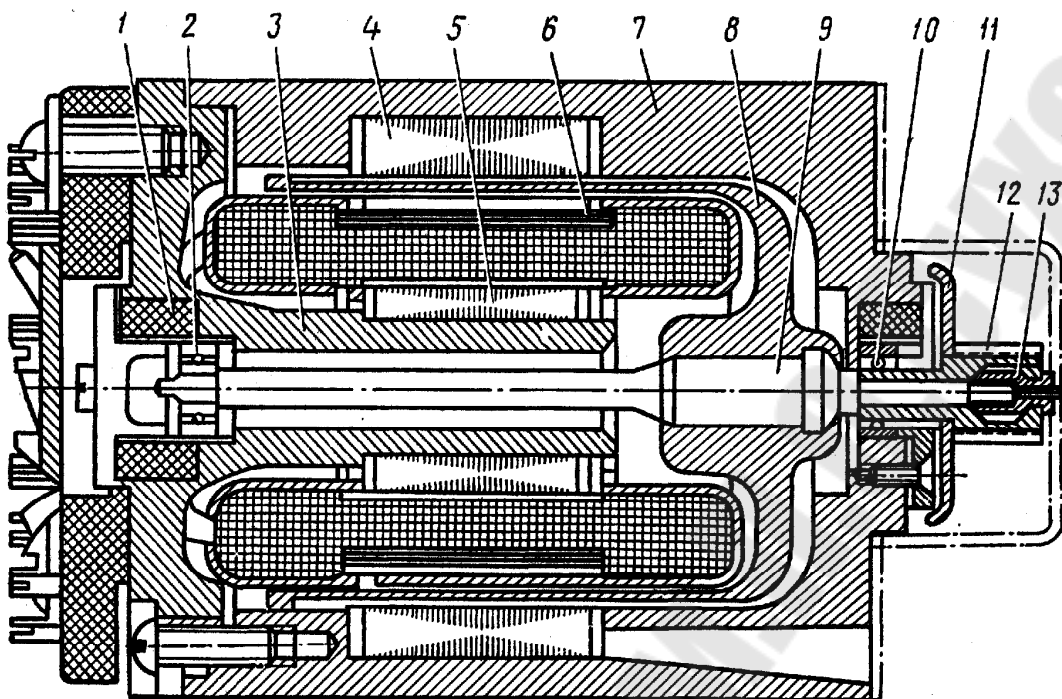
Двигатель с полым немагнитным ротором ДИД-0,6-ТВ:
